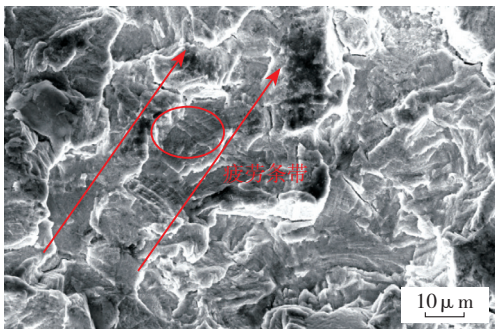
左侧横向裂纹疲劳断口微观形貌
